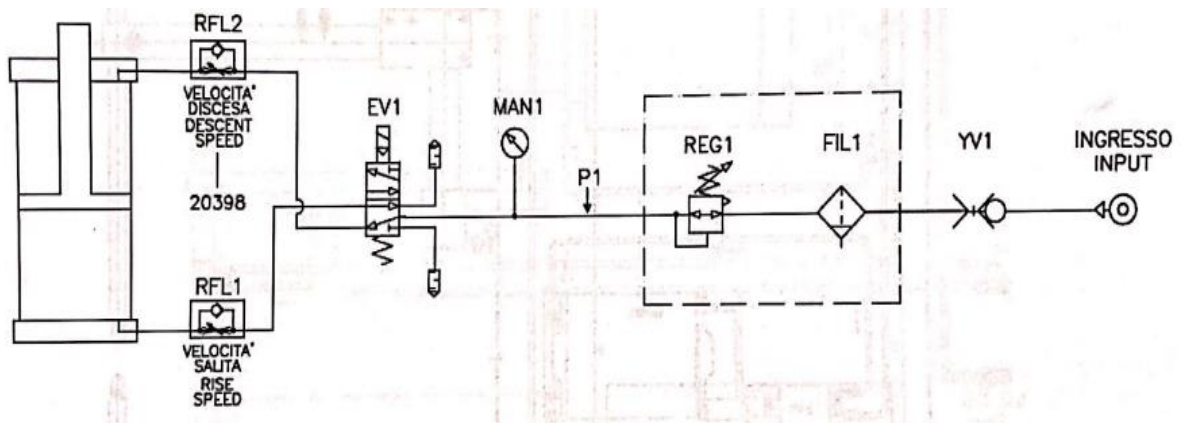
Esquema de la Electroválvula de la Soldadora de Punta.
